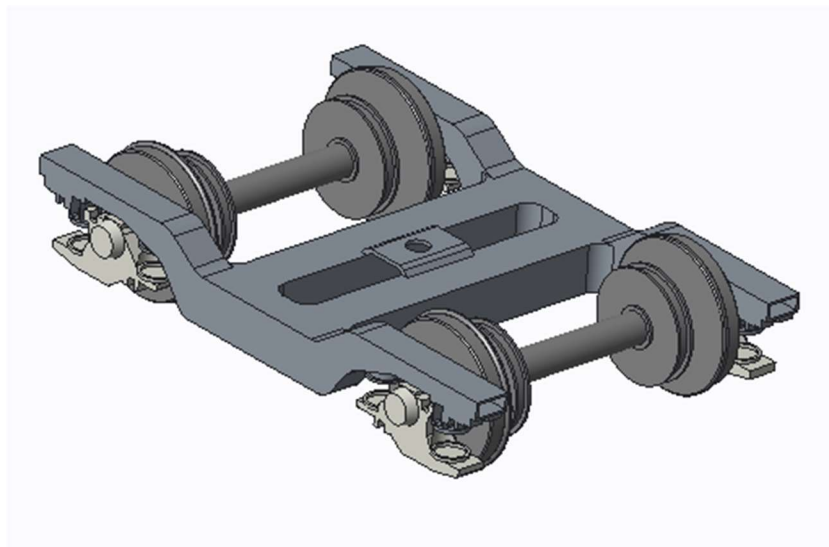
Partes del bogie de la serie 446 ensambladas en Creo Parametric
